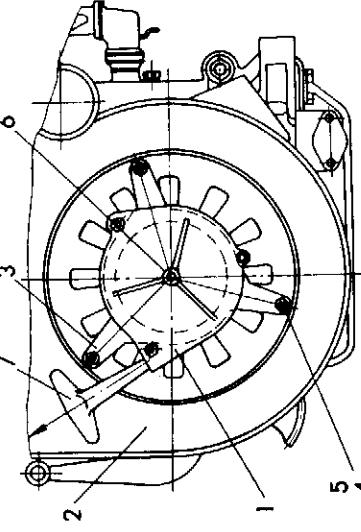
Схема установки стартера ПД-8 на двигатель:
